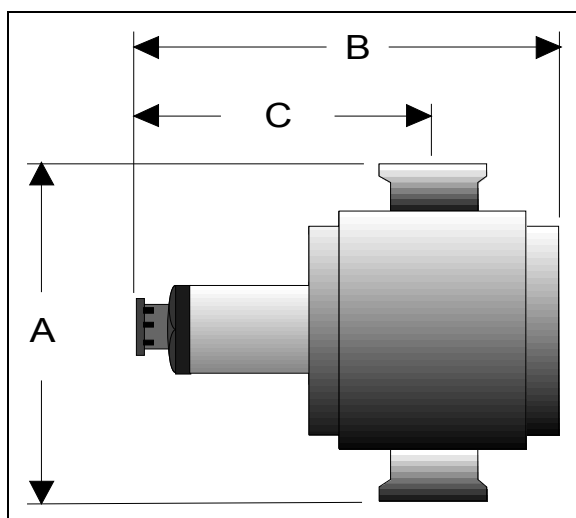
Encombrement et dimension du transmetteur modèle 622
